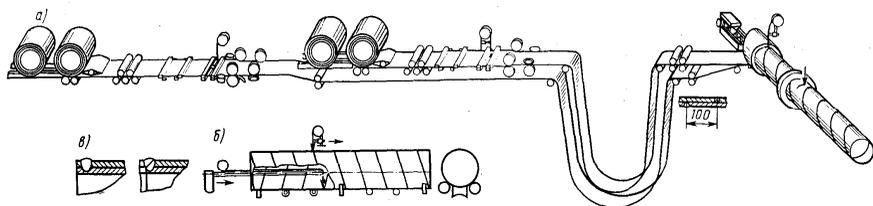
Схема изготовления двухслойных труб со спиральным швом:
